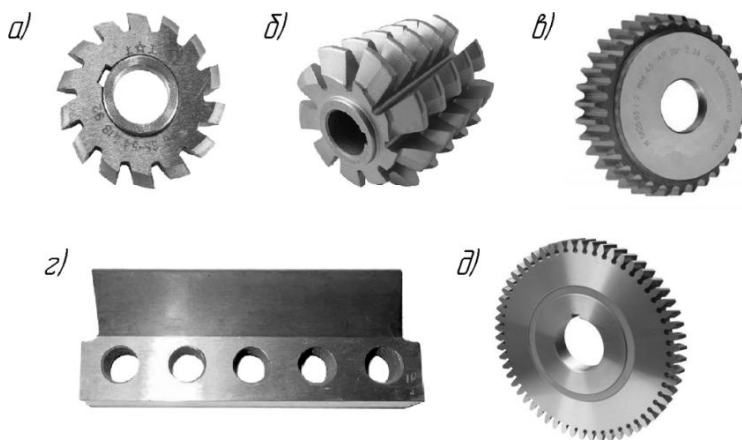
Основной инструмент зубообрабатывающих станков:
